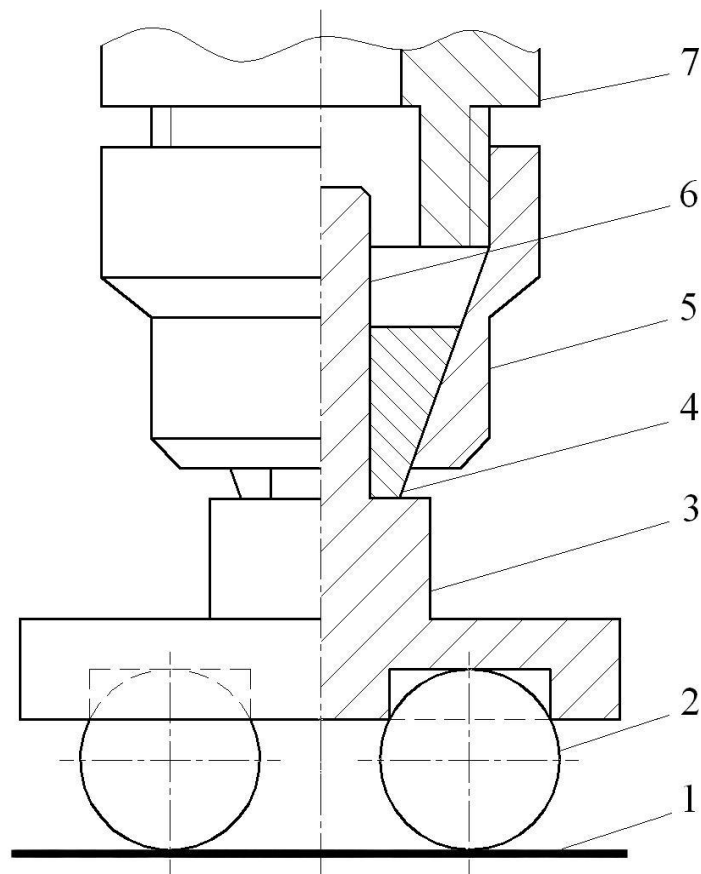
Робочий елемент установки тертя кочення: 1 – зразок; 2 – контр-тіло; 3 – обойма; 4 – затискний кулачок; 5 – гайка; 6 – хвостовик; 7 – патрон
